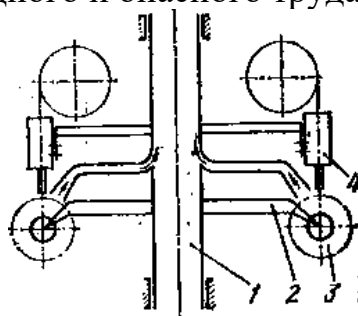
Роторный автомат для сборки и сварки тракторных катков
